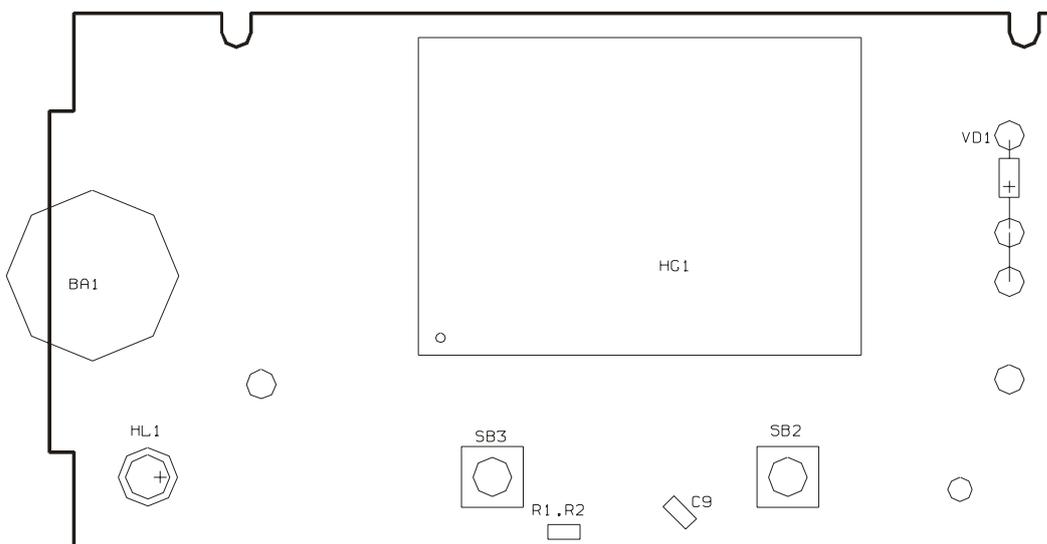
Сборочный чертеж платы обработки ТПГ-94.1. Вариант исполнения 1. Сторона пайки.
